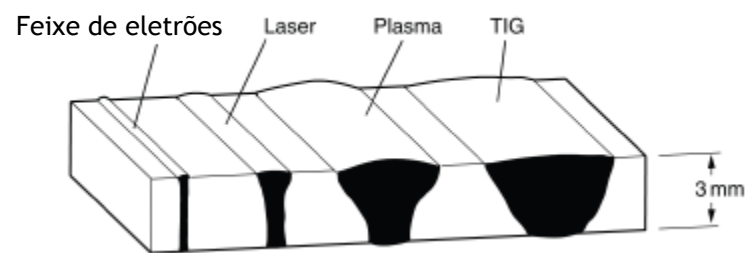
Perfis de cordões de soldadura de alguns processos
